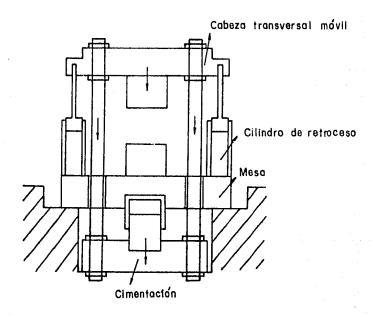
b CONJUNIO BASTIDOR-CILINDRO MOVIL
